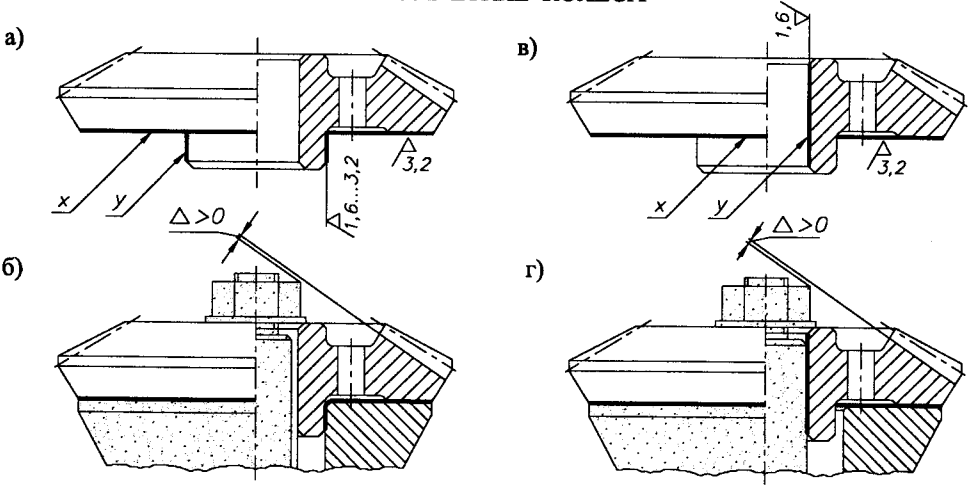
Установочные базы для нарезания зубьев на зубчатых колесах
